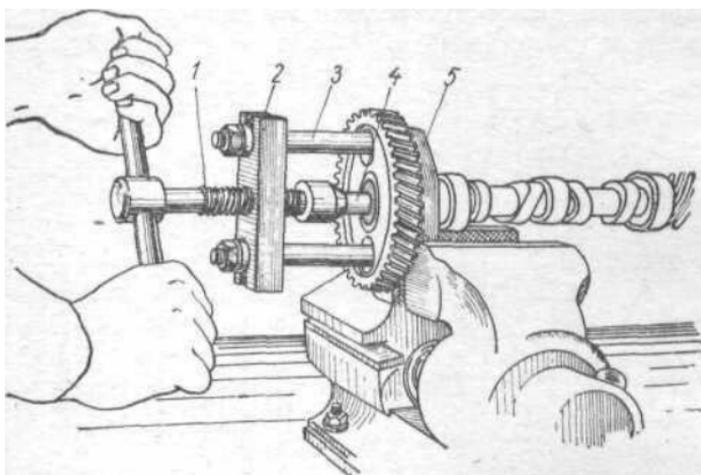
Выпрессовка шестерни распределительного вала при помощи съемника
